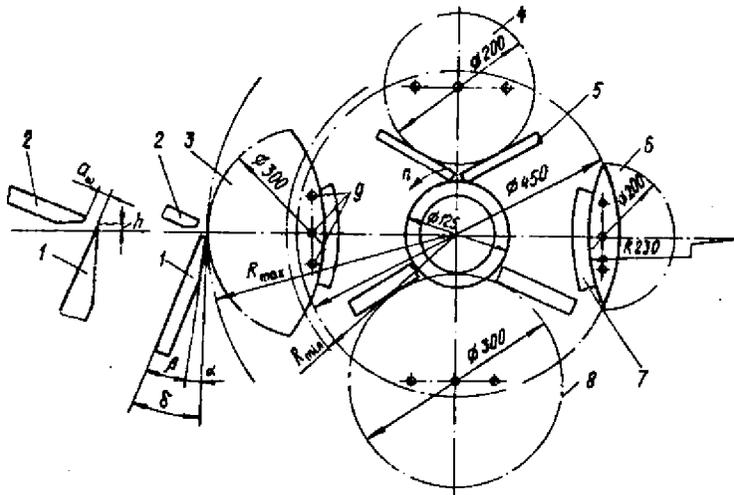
Схема строгания шпона: 1 – нож; 2 – прижимная линейка; 3, 6 – заготовки после перекантовки; 4 – заготовка; 5, 7 – опорные пластины
